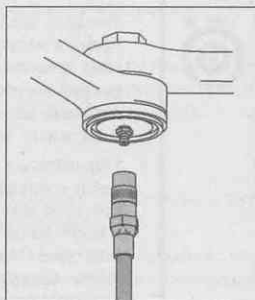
Смазочный шприц с переходником и пресс-масленка
